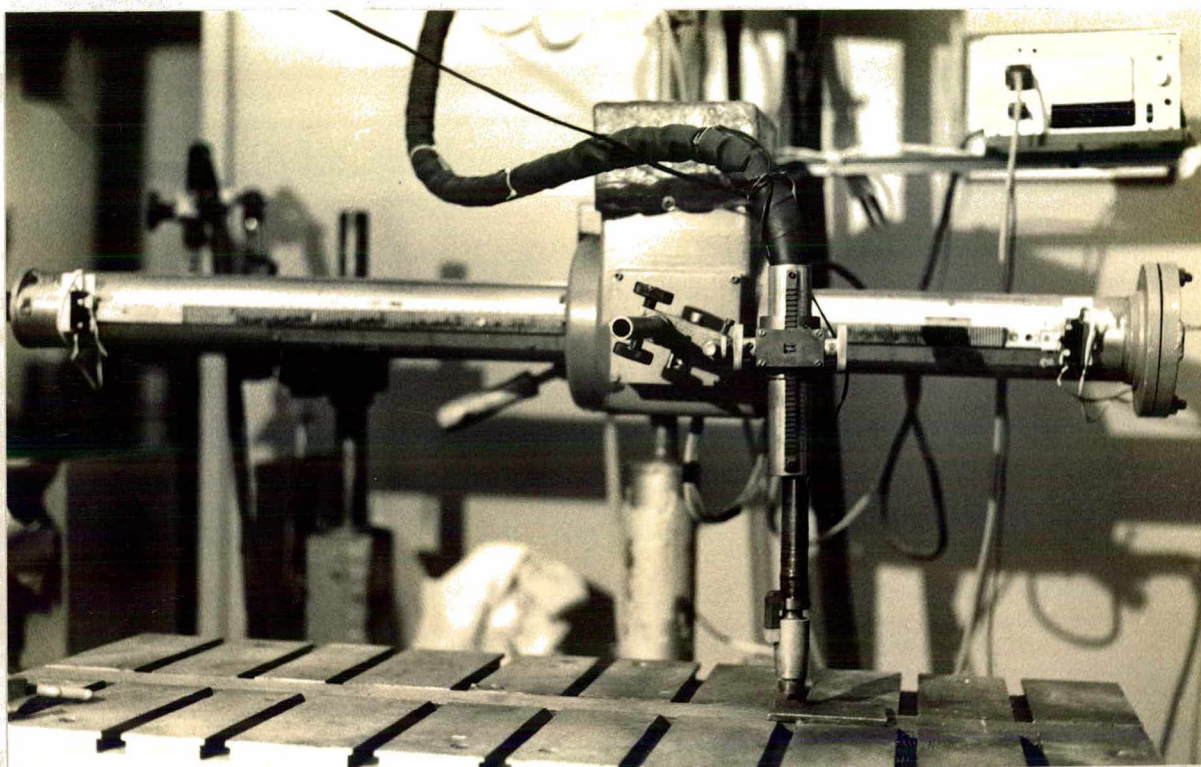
Dispositivo de condução da pistola de soldagem.
